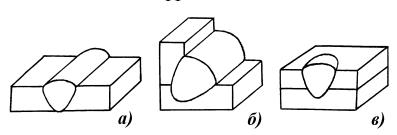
Типы сварных швов: а - стыковой; б - угловой; в – прорезной
